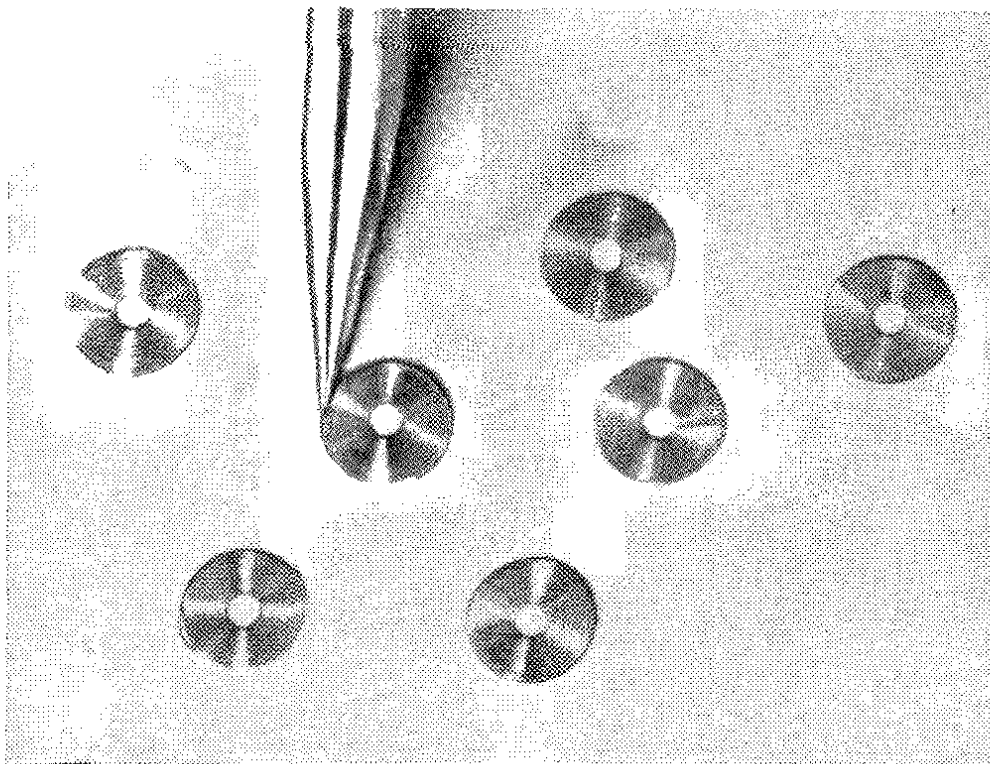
Заготовки спиралей перед отрезкой внутреннего витка
